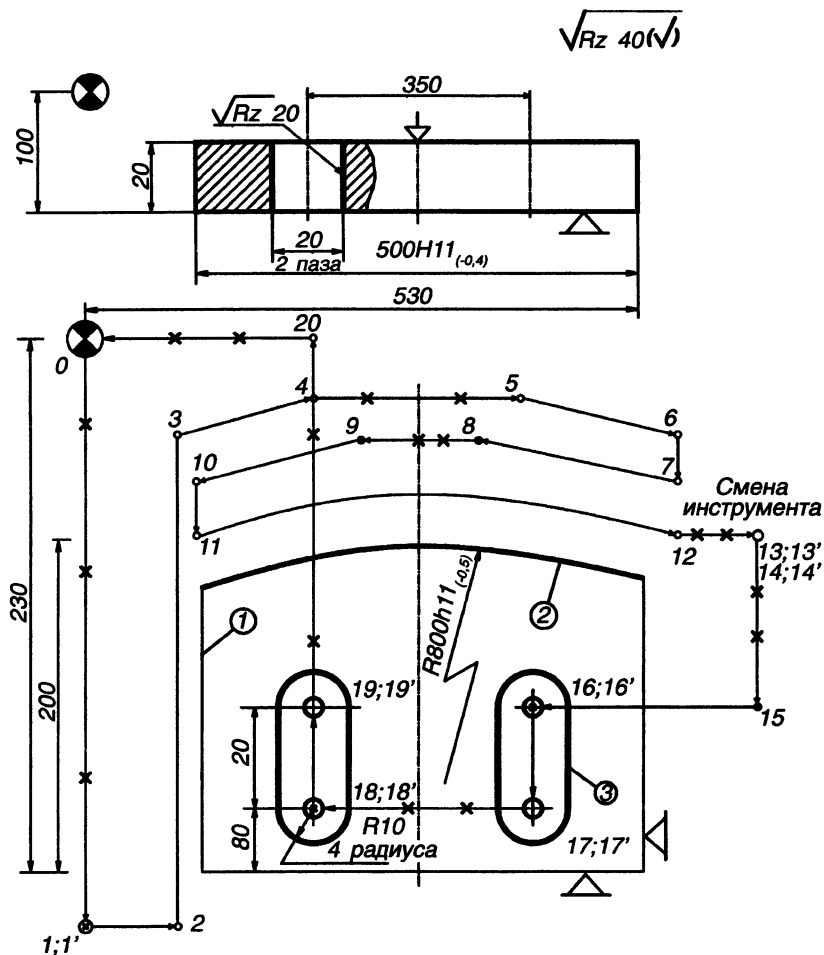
Эскиз детали для примера нормирования операции контурного фрезерования
